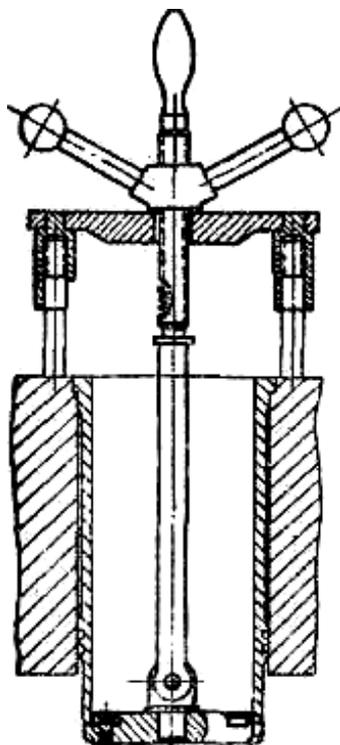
Приспособление для выпрессовки гильз цилиндров.
